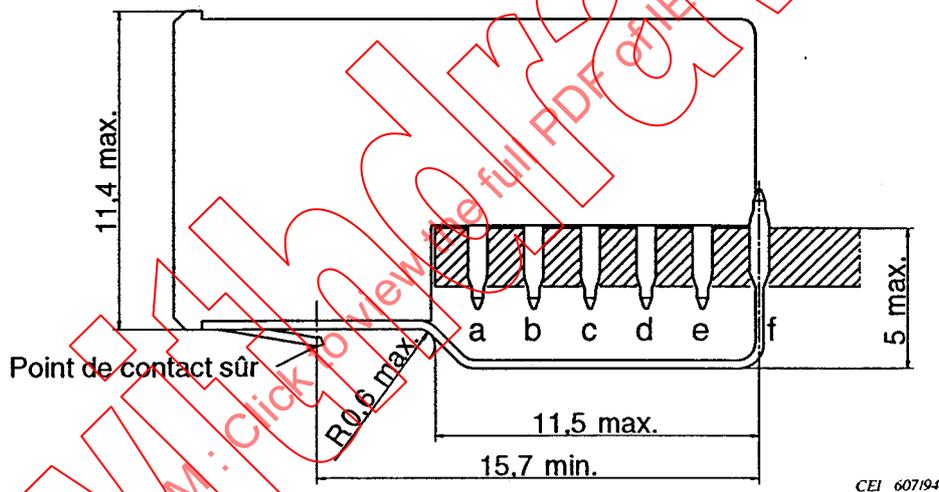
Dimensions d'accouplement de la coquille de blindage de la rangée z
